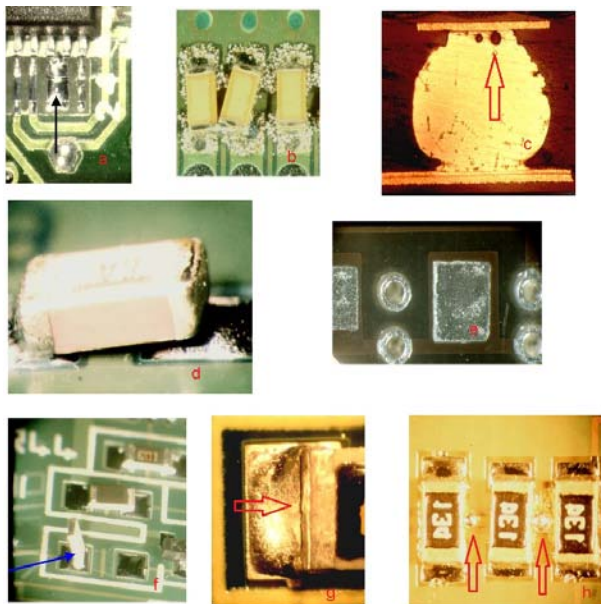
Falhas comuns no processo de soldagem SMT. (a) Curto entre terminais, (b) Falha na refusão, (c) Vazio de solda, (d) Componentes levantados, (e) Solda granulada, (f) *Tombstoning* – Componente levantado na horizontal, (g) Trincas e (h) Bolas de solda. Fonte: <http://smd-on-line.com>.
